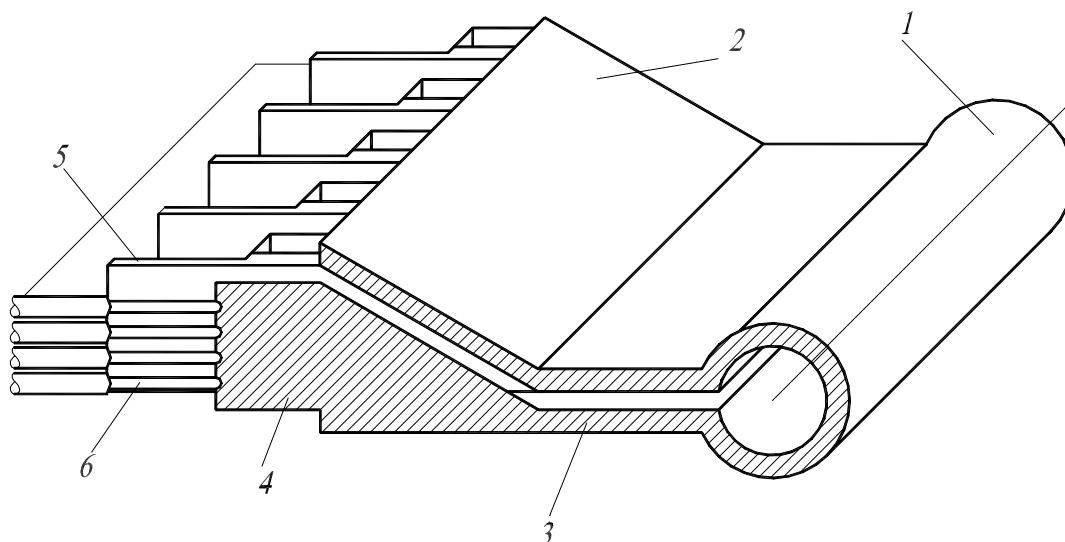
Зубчатые сборные шины: 1 - нагрузка, 2 - верхняя шина, 3 - нижняя шина, 4,5 - зубья, 6 - разделка кабелей
